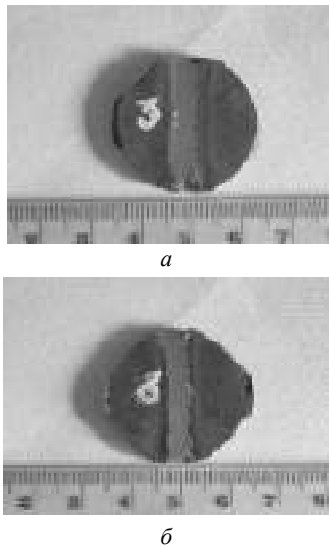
Внешний вид поверхности образцов-темплетов после сварки промышленного литейного свариваемого жаропрочного коррозионностойкого сплава ЖСЗЛС: *a* – единичные точечные свечения в сварном шве (присадка ЭП367); *б* – единичные точечные свечения по границе сварного шва (присадка ЖСЗЛС-М)
